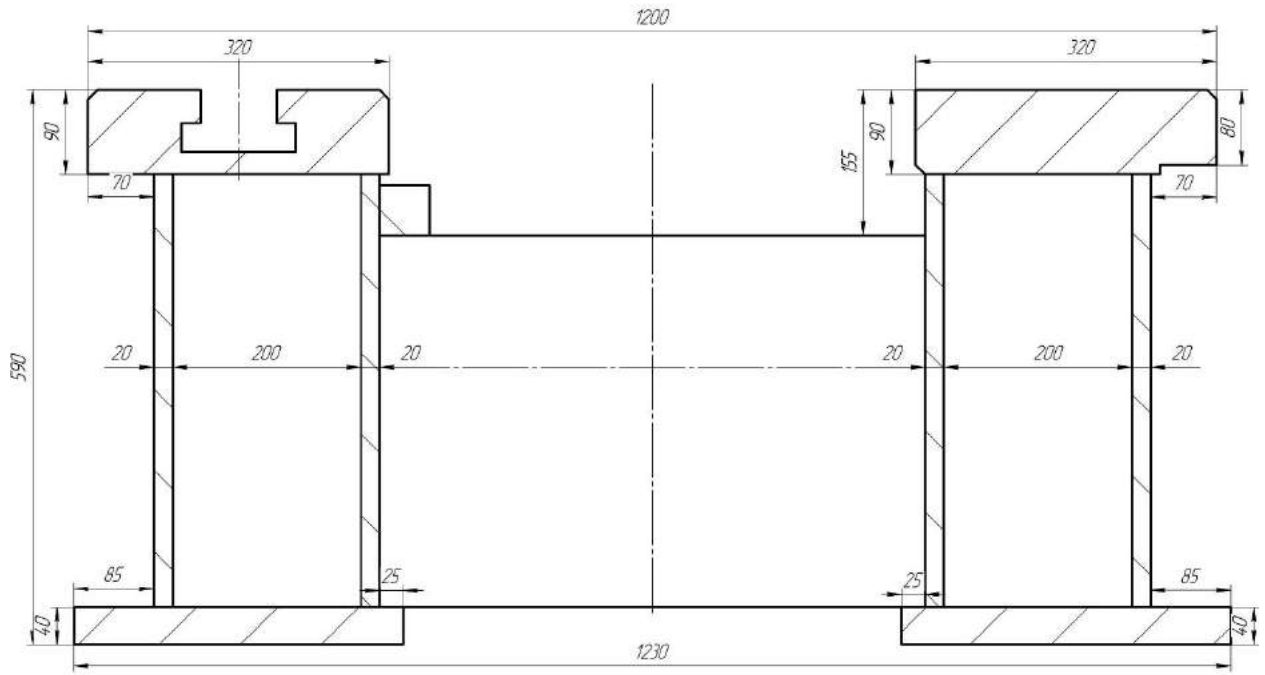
Поперечний розріз зварної станини виробу верстата 1К670Ф3
